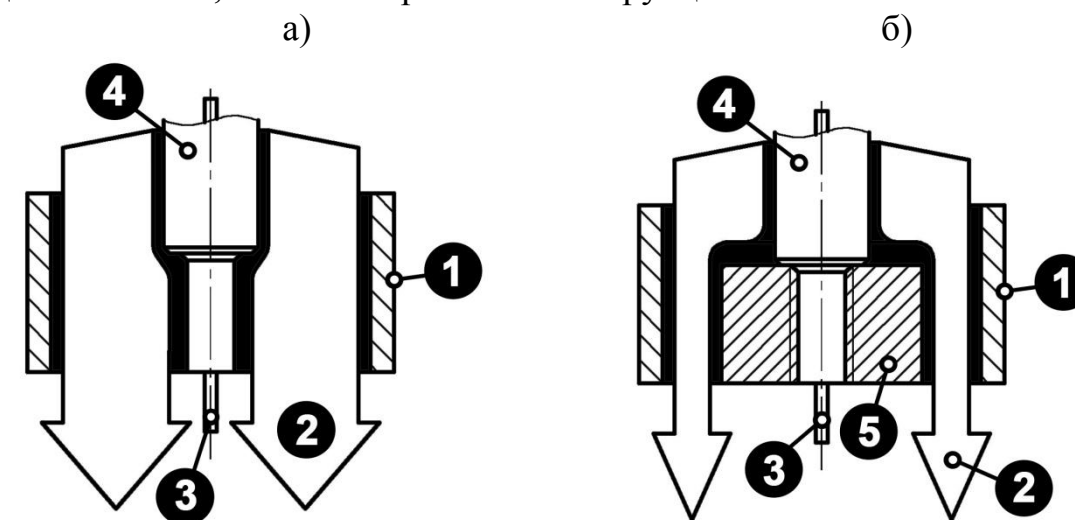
Схемы подачи защитного газа в зону сварки при традиционном и комбинированном способе газовой защиты: а – схема с традиционной подачей защитного газа в зону сварки; б – схема с кольцевой подачей защитного газа; 1 – сопло сварочной горелки; 2 – поток защитного газа (CO_2); 3 – электродная проволока; 4 – токоподводящий наконечник; 5 – втулка для распределения газового потока
